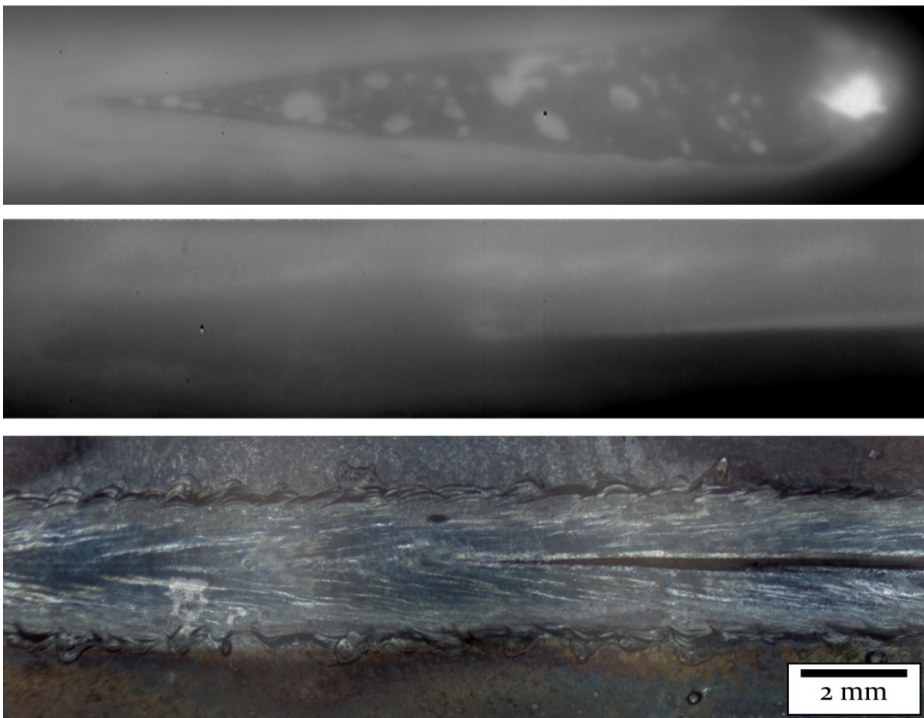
Oben: Einzelbild einer exemplarischen Schmelzbadgeometrie aus einer Thermografieaufnahme, Mitte: Einzelbild des im Schweißprozess entstandenen Nahtmittentrisses, Unten: Aufsicht der Schweißnaht mit Nahtmittentriss; $P = 6,00 \text{ kW}$; $v_L = 60 \text{ mm/s}$; $E = 100 \text{ J/mm}$; $d_F = 170 \text{ }\mu\text{m}$
